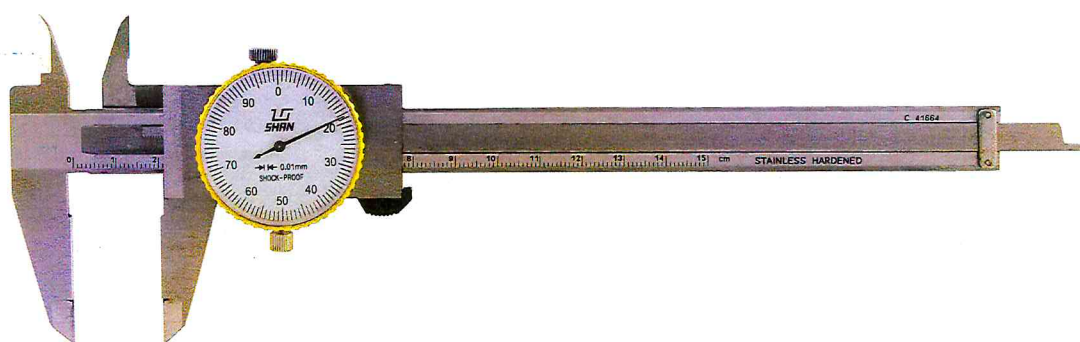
Общий вид штангенциркулей двусторонних с глубиномером с отсчетом по круговой шкале
